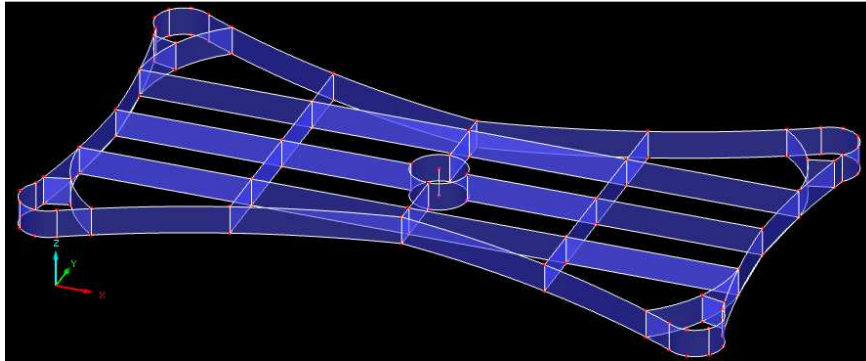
Reforzado de la cubierta superior de la torre (Fuente propia)
